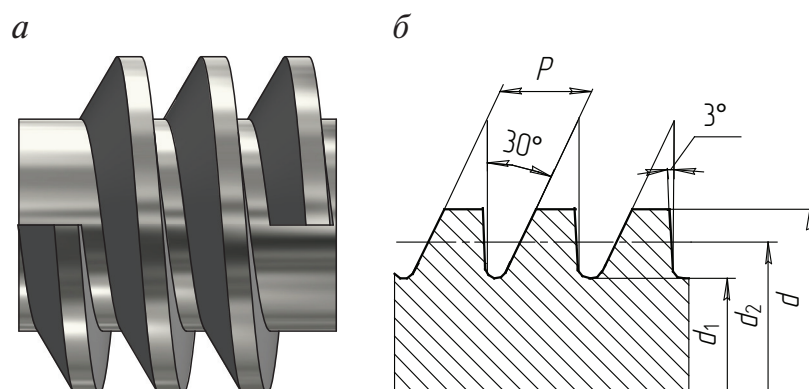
Изображение (а) и профиль (б) упорной резьбы
